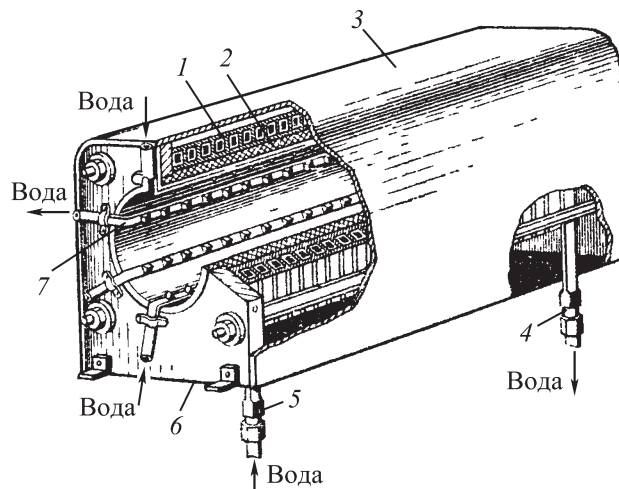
Индуктор для сквозного нагрева цилиндрических заготовок
